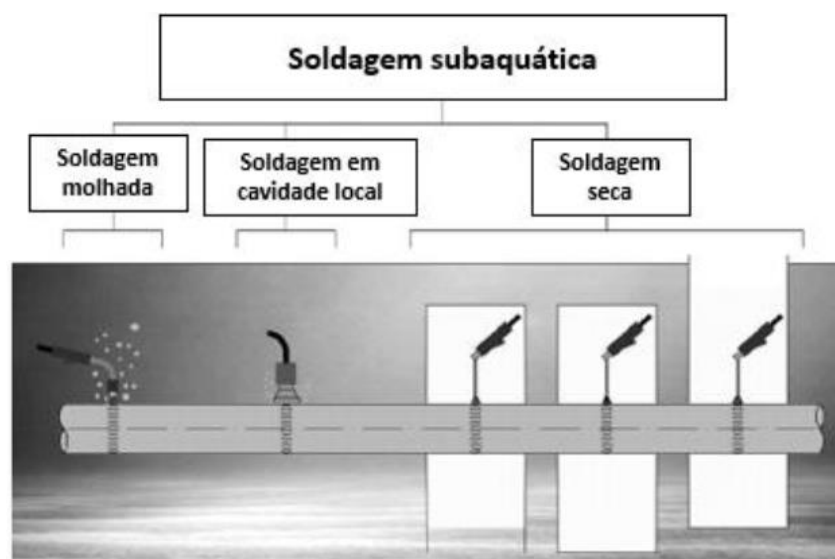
Classificação das técnicas de soldagem subaquática.
